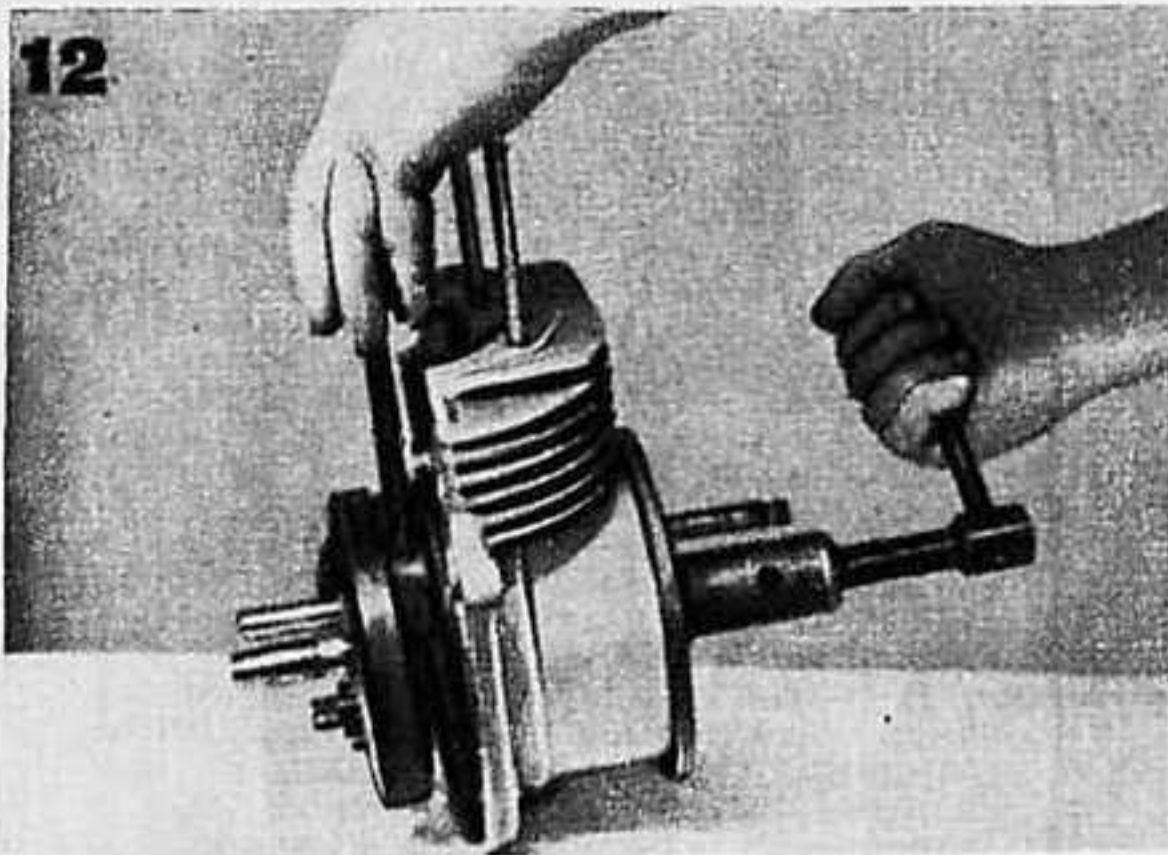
Извлечение коленчатого вала двигателя из левой половинки картера.
